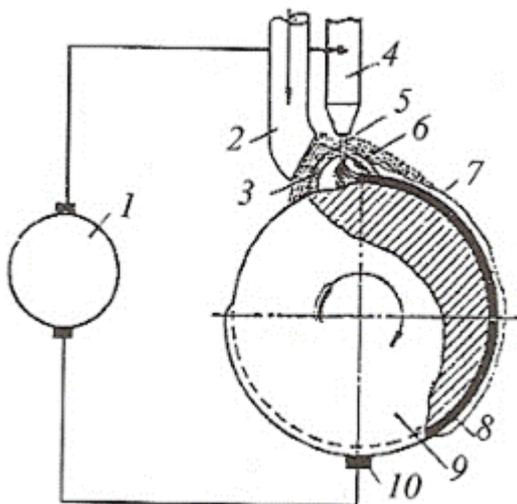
Схема горения электрической дуги под слоем флюса: 7 — источник тока для питания дуги; 2 — устройство для подачи флюса; 3 — оболочка для жидкого флюса; 4 — мундштук; 5 — электродная проволока; 6 — электрическая дуга; 7 — шлаковая корка; 8 — наплавленный слой; 9 — наплавляемая деталь; 10 — подвод тока к детали
